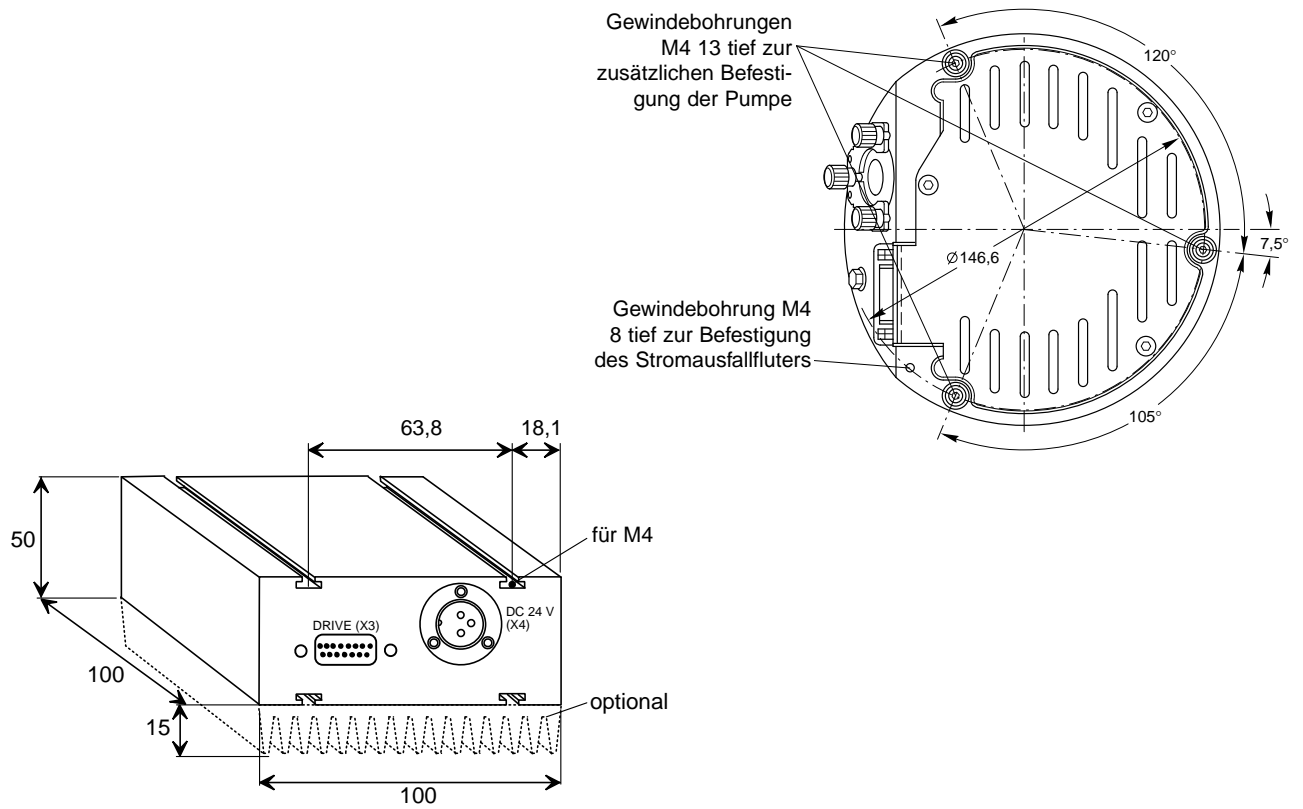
Maßzeichnung des Frequenzwandlers und Boden der Pumpe; Maße in mm
